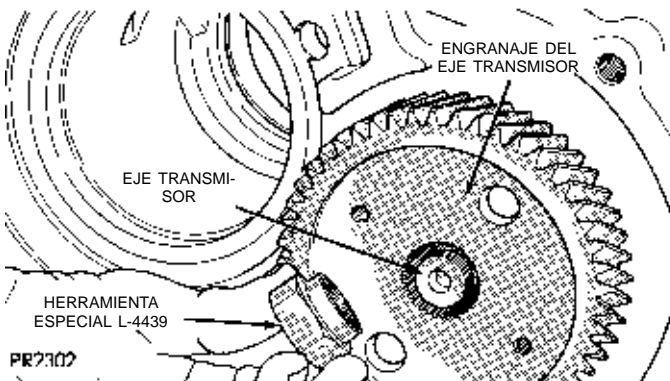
Colocación del engranaje del eje transmisor en el eje transmisor
